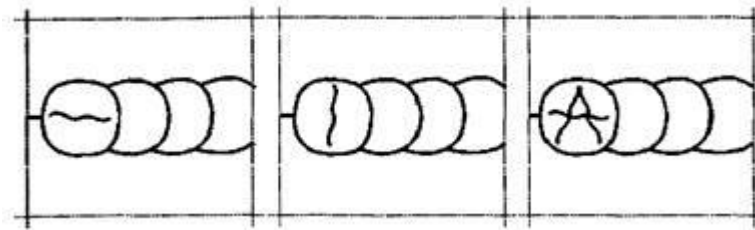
Кратерная трещина сварного соединения
